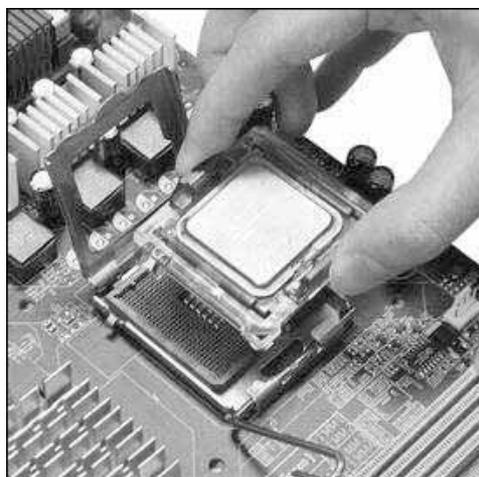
Установка процессора Pentium 4 в разъем Socket 775
